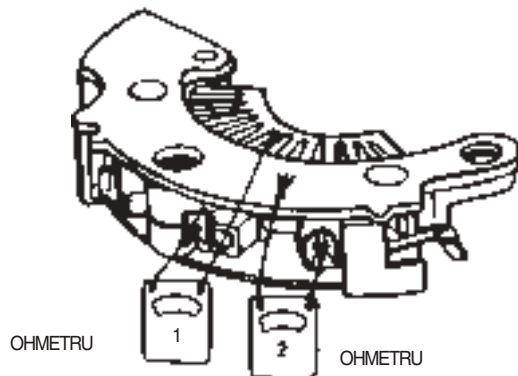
Alternatorul CS 130 - demontare, testare, montare
